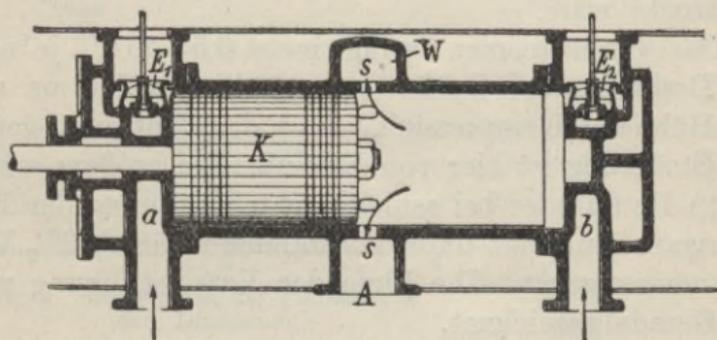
Zylinder einer Gleichstromdampfmaschine.
